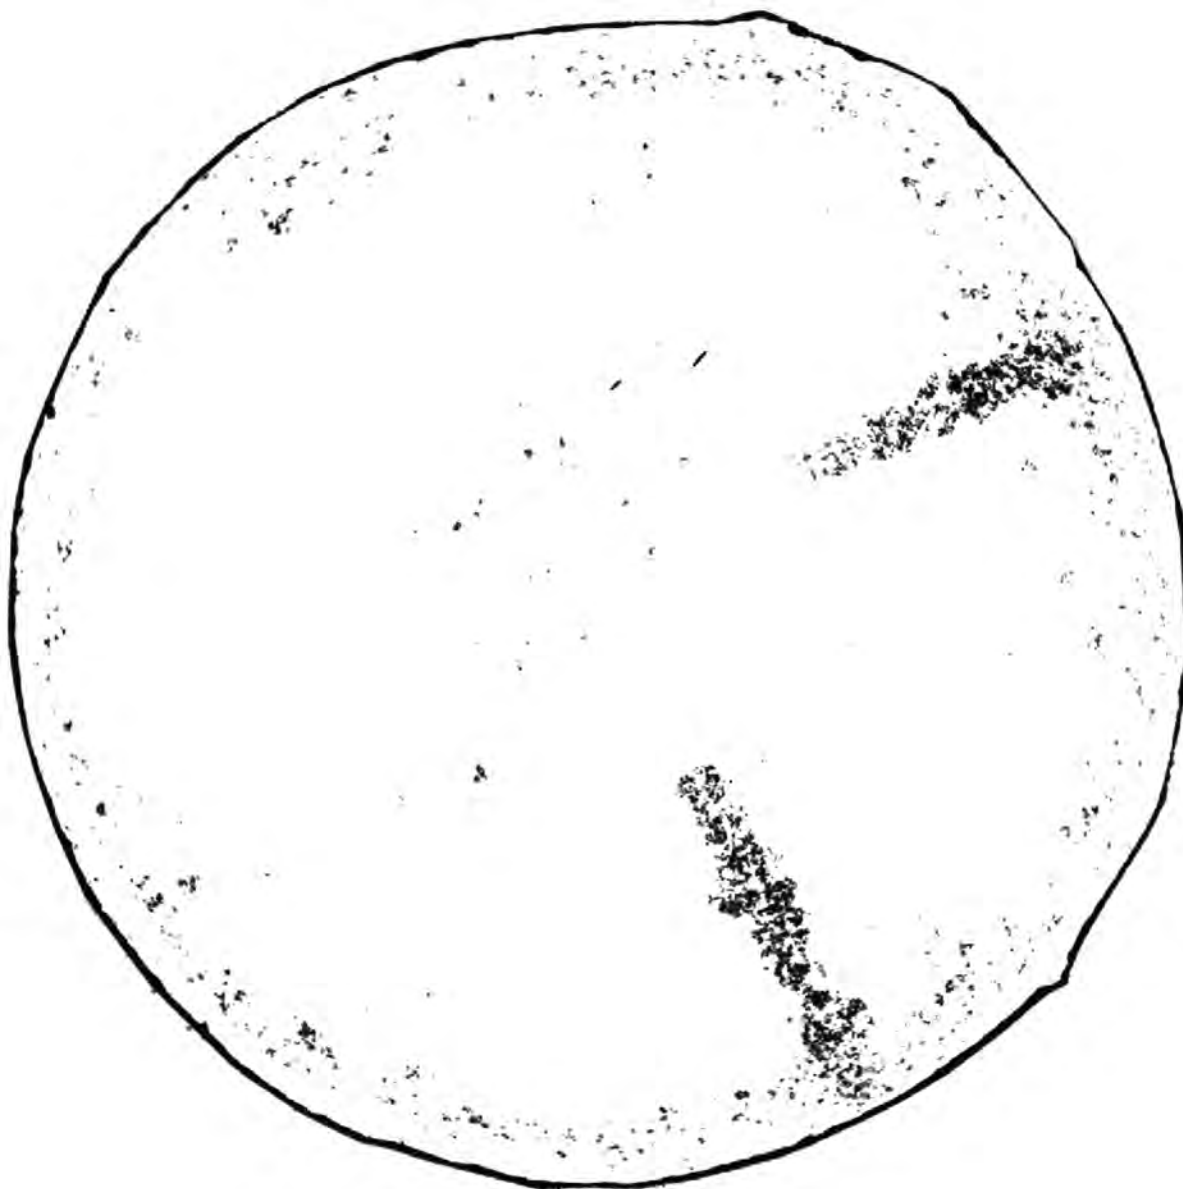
Серный отпечаток диска № 5 верхней шейки Ø330 мм с неметаллическими включениями MgS под термозащитными чехлами термопар
